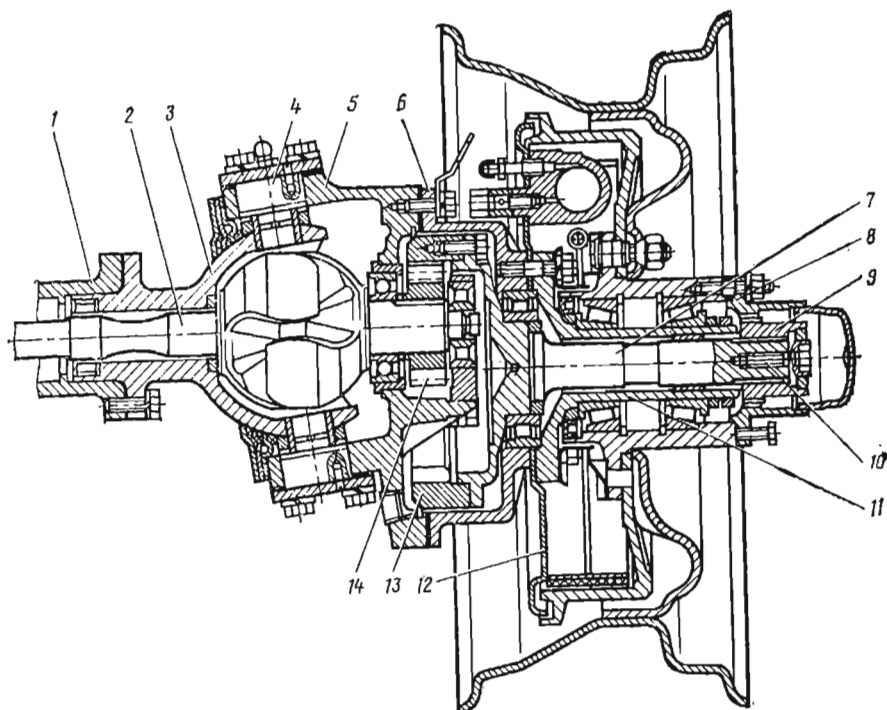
Привод управляемого переднего колеса автомобиля УАЗ-469
